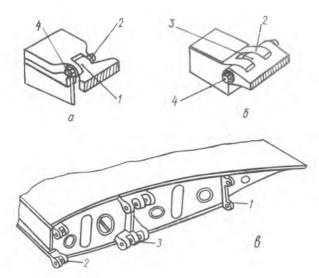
Вильчатые стыки: а — элементарный узел "ухо-вилка"; б — элементарный узел "вилка — гребенка"; в — стыковой узел "ухо-вилка-гребенка"; І — ухо; 2 — вилка; 3 — гребенка; 4 —стыковой болт
